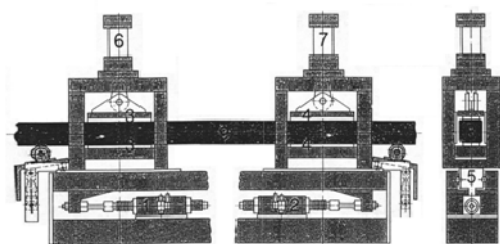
Схема устройства балочного типа для вытягивания заготовки конструкции фирмы Mannesmann-Demag
